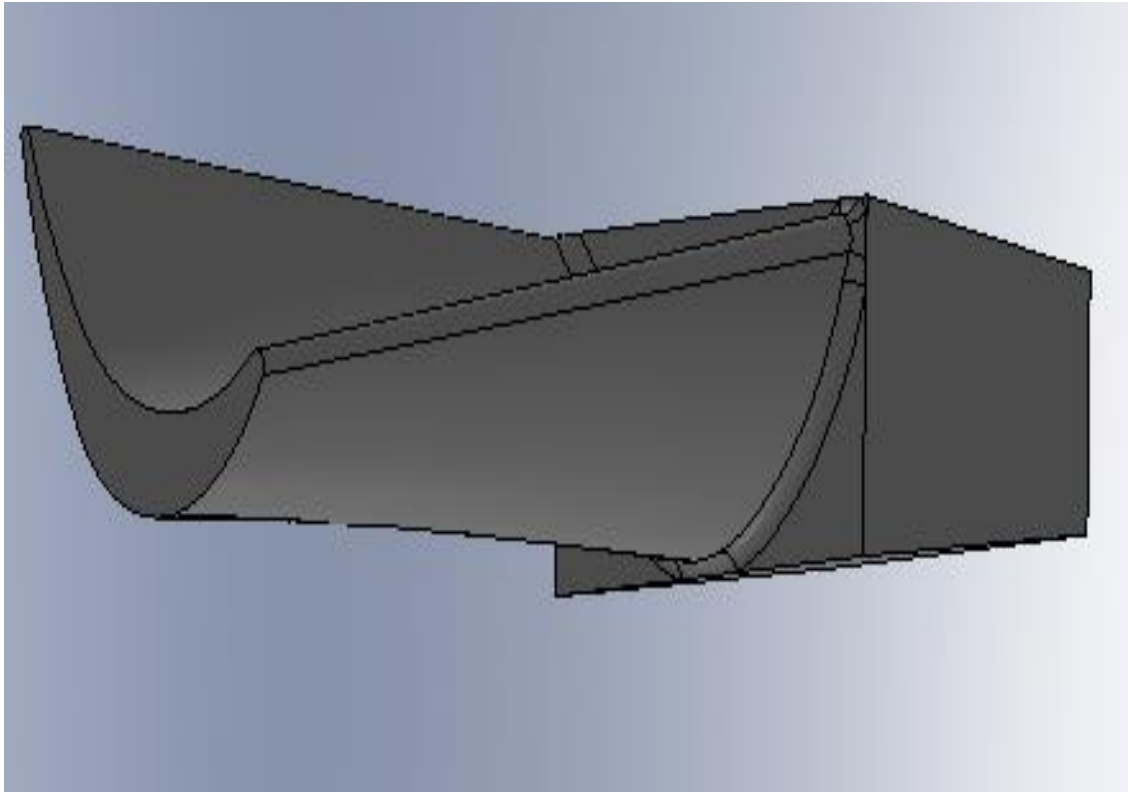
Pièce complexe (surface gauche, ailette de turbine)
